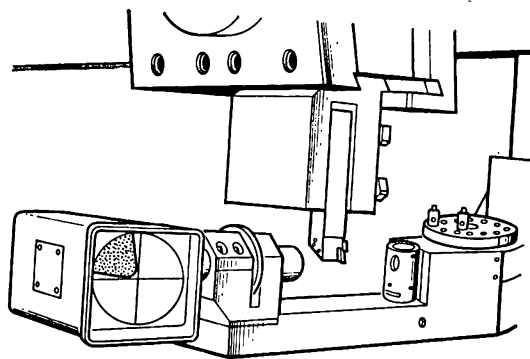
Схема прибора для настройки вылета инструмента в резцедержателе на станке
